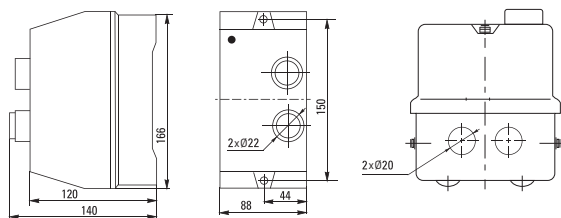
Габаритные размеры для ПМЛ 9-18А
